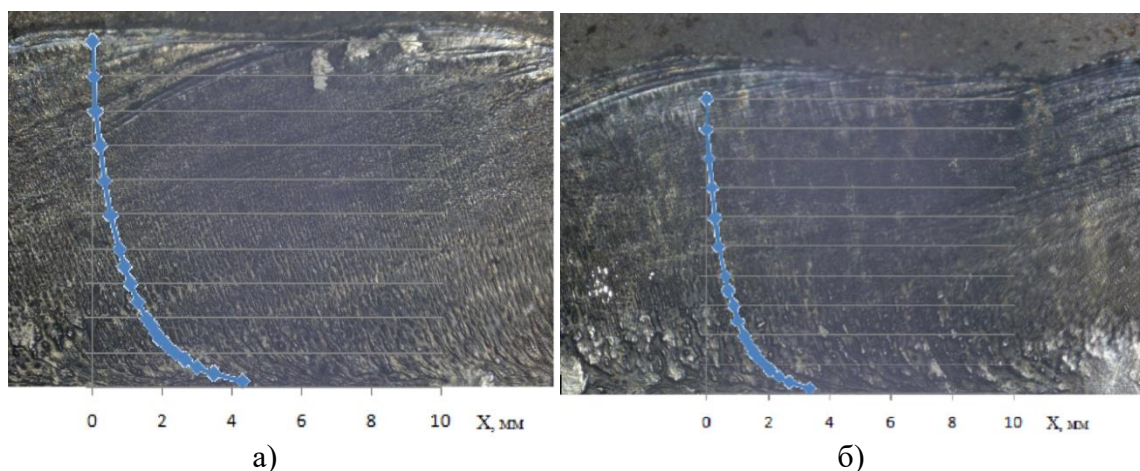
Сравнение реальных и расчётных форм кристаллитов сварных швов: а – сварка без подогрева присадочной проволоки; б – сварка с подогревом присадочной проволоки.
